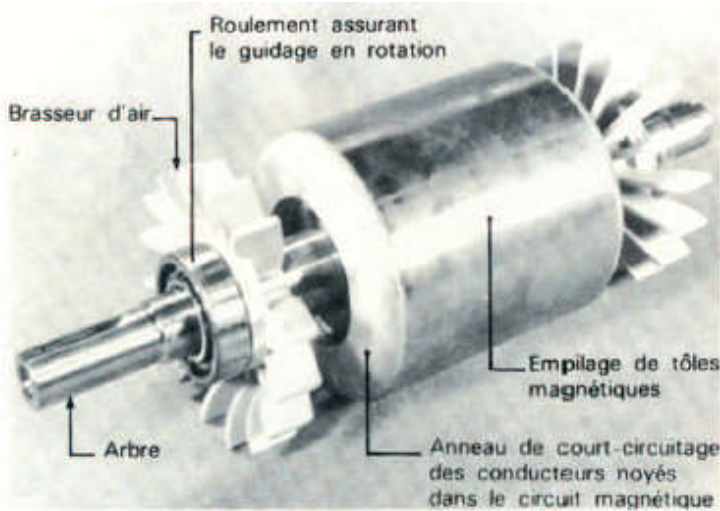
Rotor à cage d'écureuil (vue d'ensemble)
